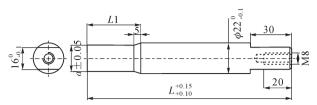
标准化后的压芯杆尺寸 Fig.4 Standardized mandrel dimensions
